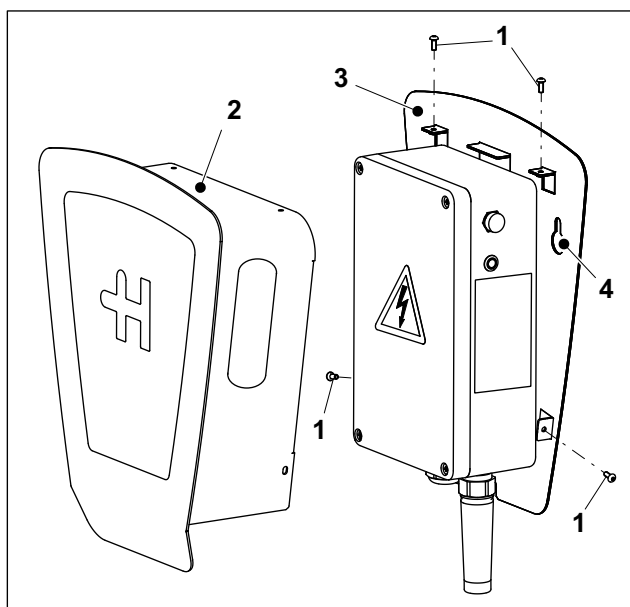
Heidelberg Wallbox Home Eco con caperuza de protección
